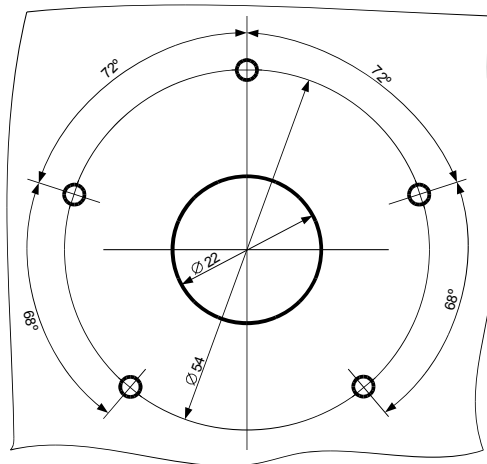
Чертеж разметки на баке для сверления отверстий для установки датчика ДУ-03.
